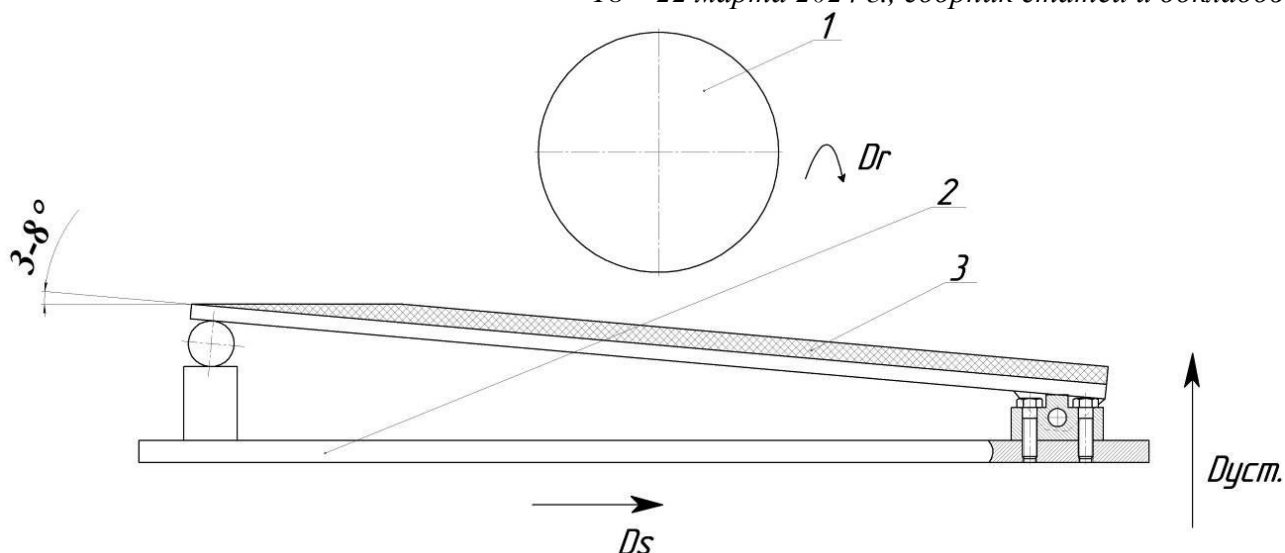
Схема обработки поверхности резиноканевой конвейерной ленты
